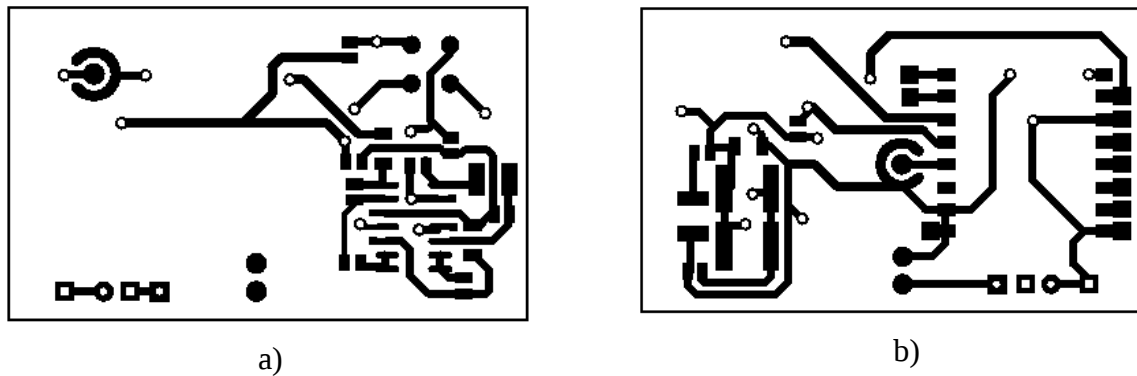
a) Capa inferior de la PCB, b) Capa superior de la PCB.
